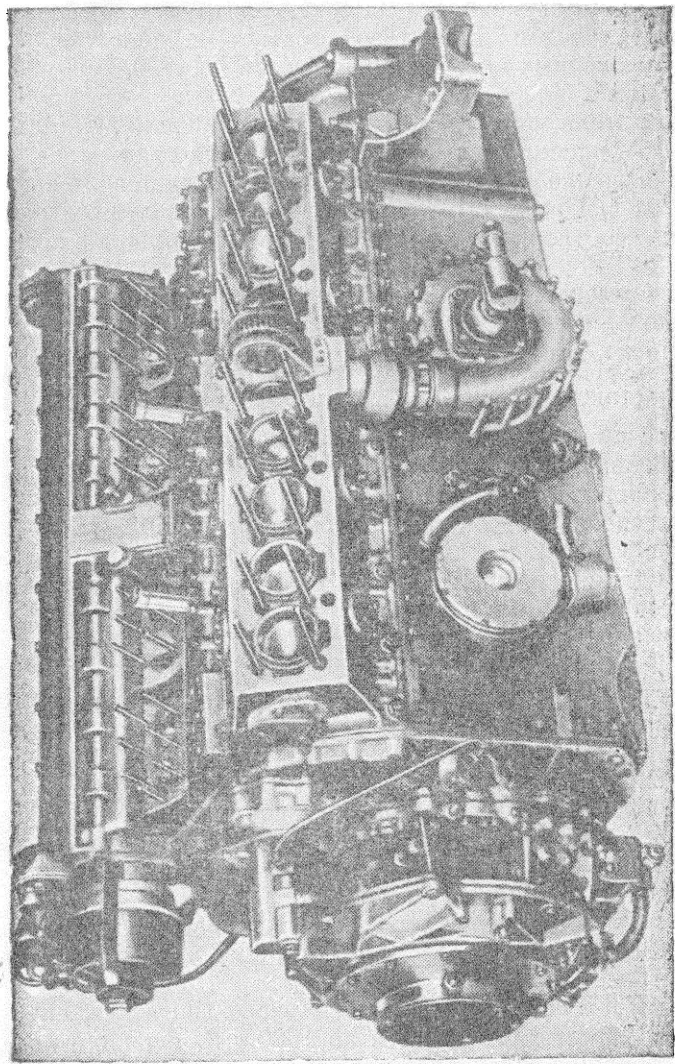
Общий вид 16-цилиндрового V-образного гоночного двигателя с нагревателем со снятой головкой одного ряда цилиндров
